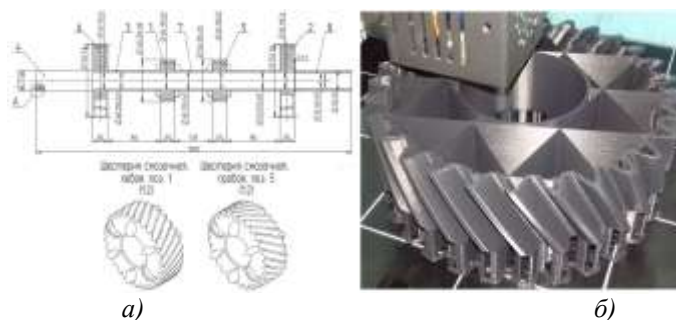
Редуктор с маслоподающего механизма и 3D печать (б) зубчатого колеса к нему
